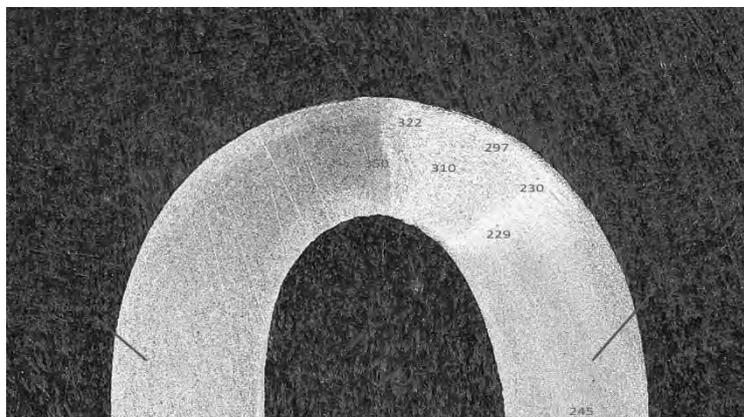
Значения твердости HV в разных зонах сварного шва
